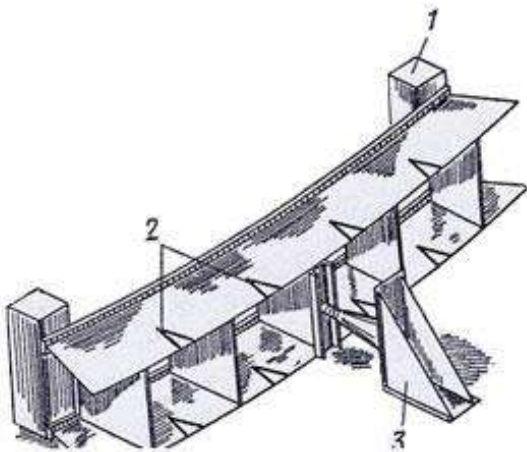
Схема корректировки сварных фундаментов термомеханической правкой с использованием домкратов. 1 – схема опор, 2 – схема мест прогрева, 3 – схема домкрата.
